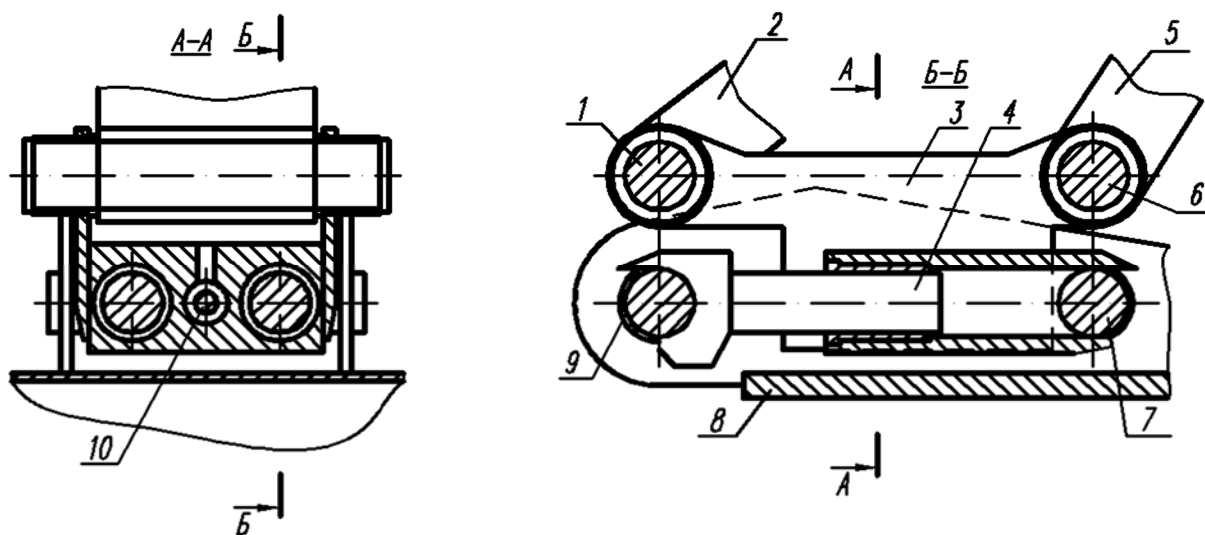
Схема захватного устройства Сабанчиева: 1, 6 – пальцы крепления захватного устройства на рабочем оборудовании экскаватора; 2 — тяга механизма поворота ковша; 3 – корпус захватного устройства; 4 – штанга; 5 – рукоять; 7 и 9 – пальцы крепления ковша к захватному устройству; 8 – ковш; 10 – шток.
